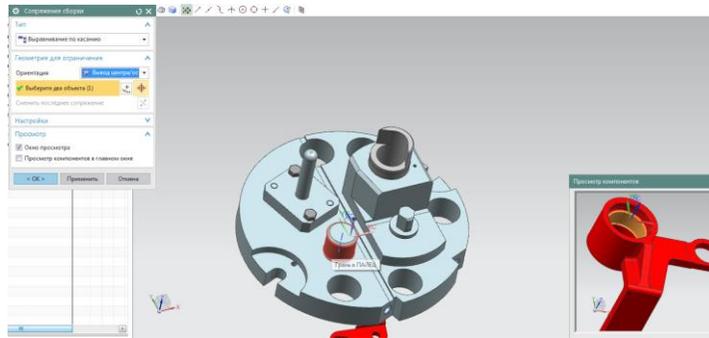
Совмещение осей базового отверстия детали «Качалка» и детали «Палец»
